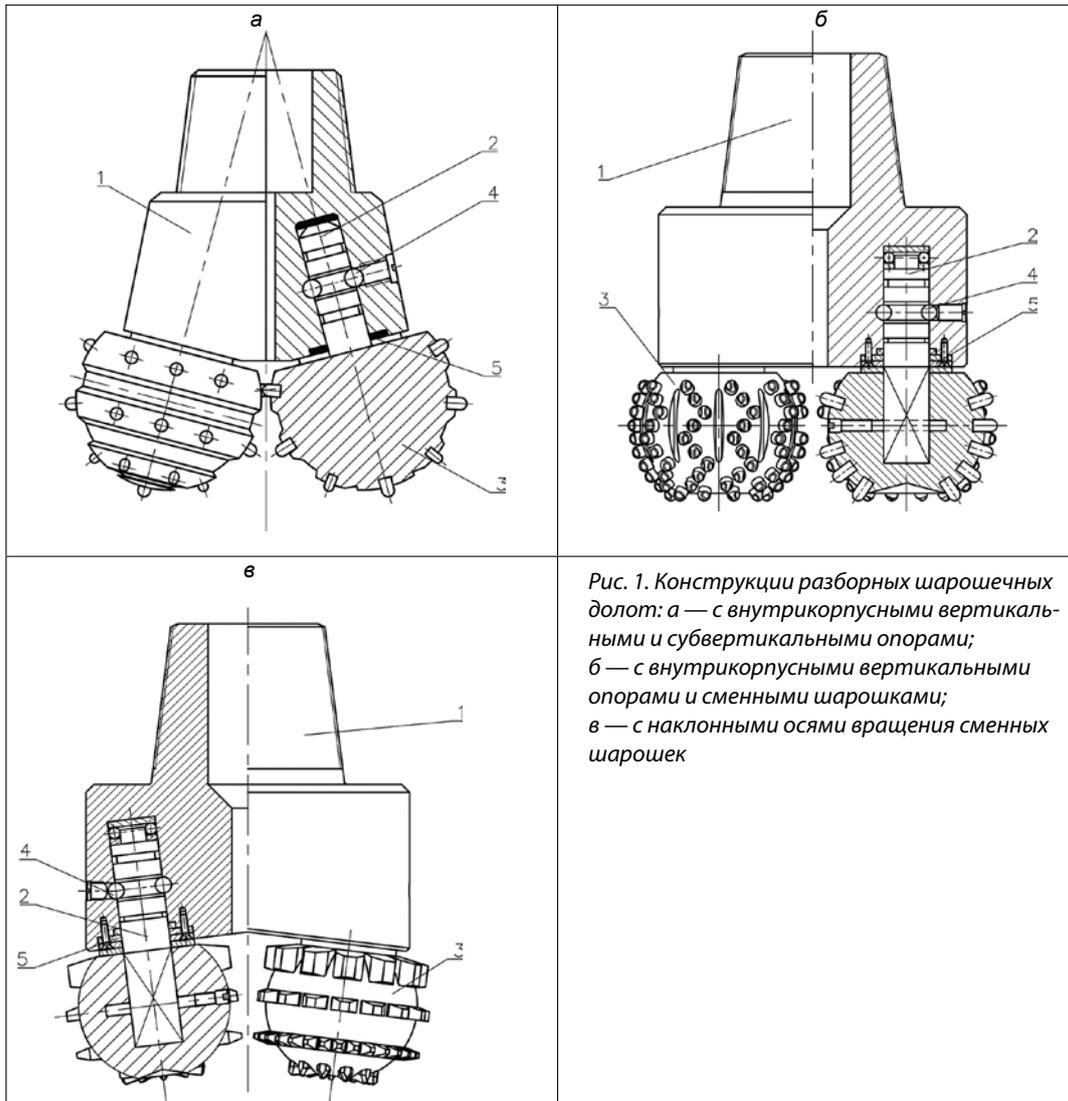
Конструкции разборных шарошечных долот: а — с внутрикорпусными вертикальными и субвертикальными опорами; б — с внутрикорпусными вертикальными опорами и сменными шарошками; в — с наклонными осями вращения сменных шарошек
